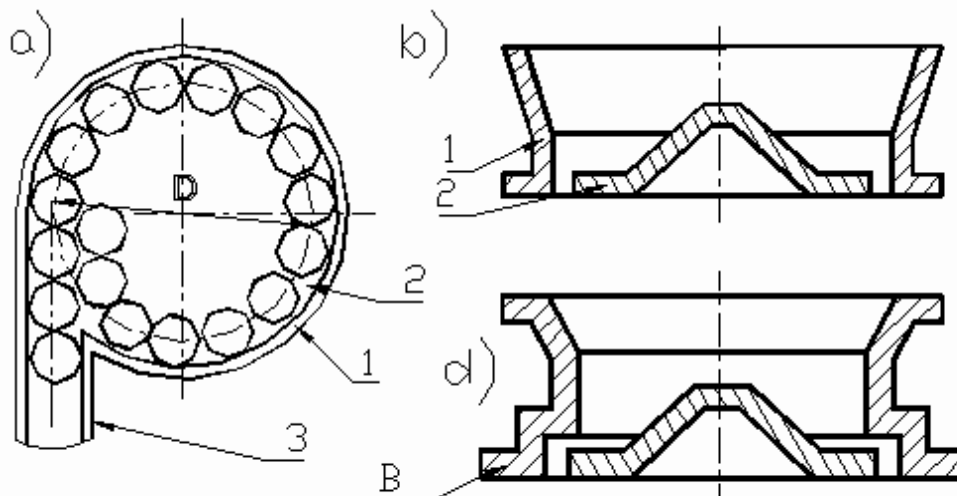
Схема бункерного загрузочного приспособления с фрикционным диском для подачи
